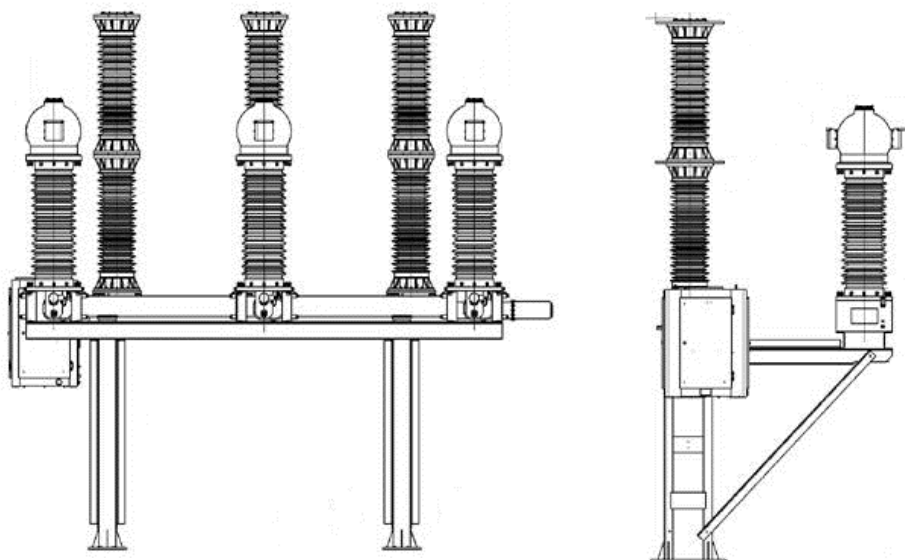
Установка выключателя ВГТ-110 и трансформатора тока
